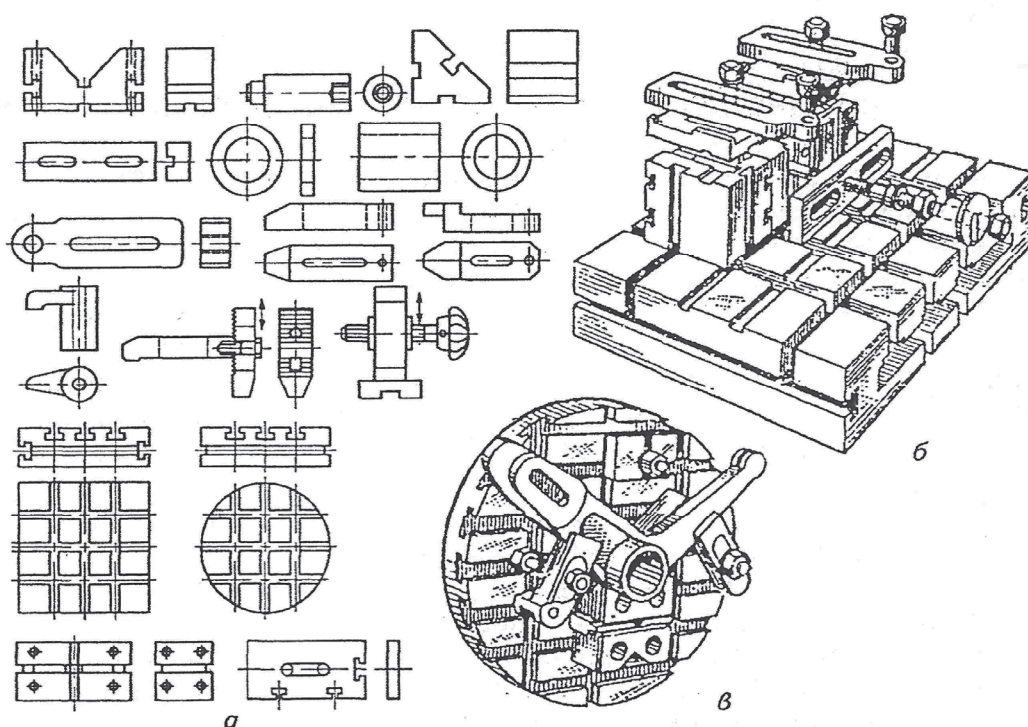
Детали комплекта УСП и собранные из них приспособления:
